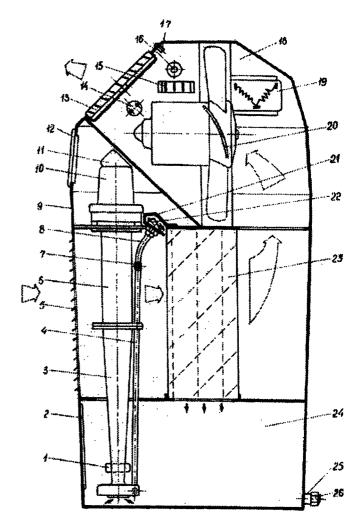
Конструктивная схема воздухоохладителя (вид сбоку)
